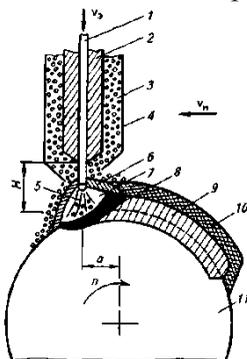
Схема наплавки под слоем флюса цилиндрических деталей:
